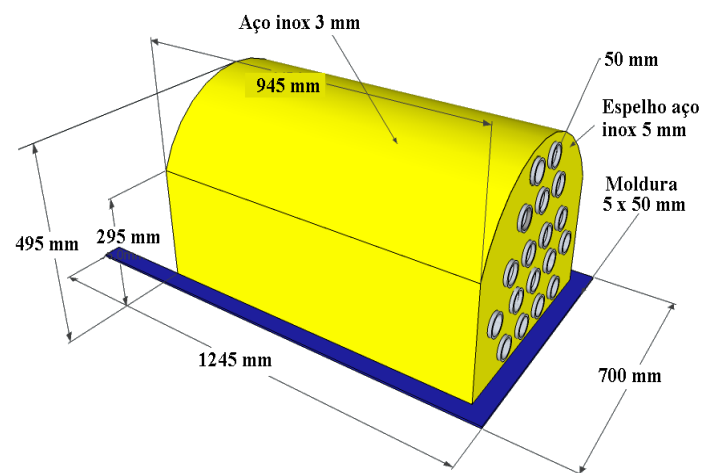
Trocador de calor com os tubos e moldura de apoio.
